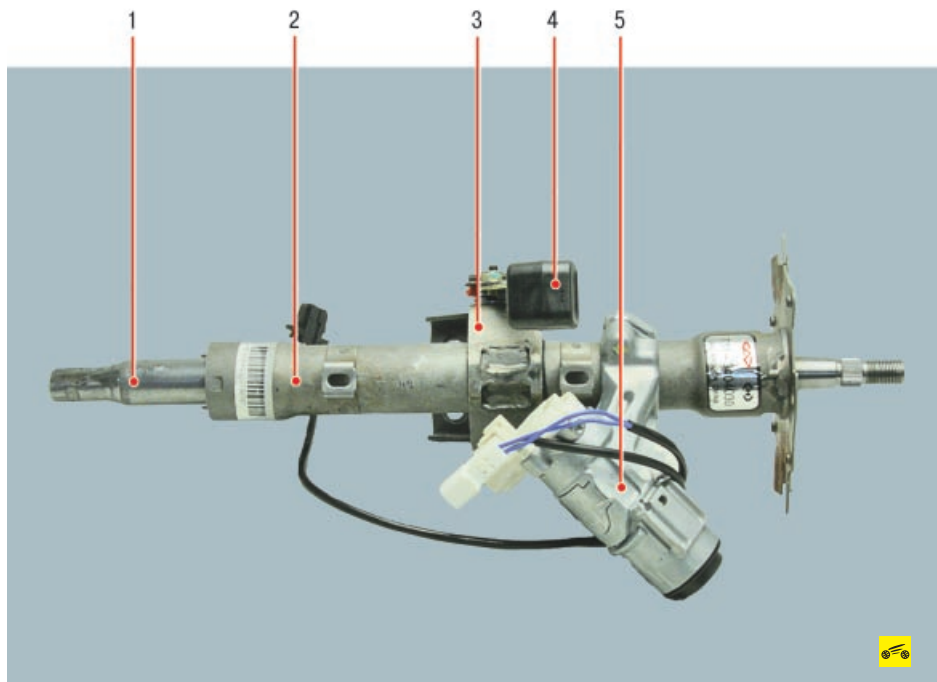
Рулевая колонка: 1 – вал рулевой колонки; 2 – кожух рулевой колонки; 3 – механизм регулировки положения рулевого колеса; 4 – блокирующая рукоятка механизма регулировки положения рулевого колеса; 5 – замок зажигания
